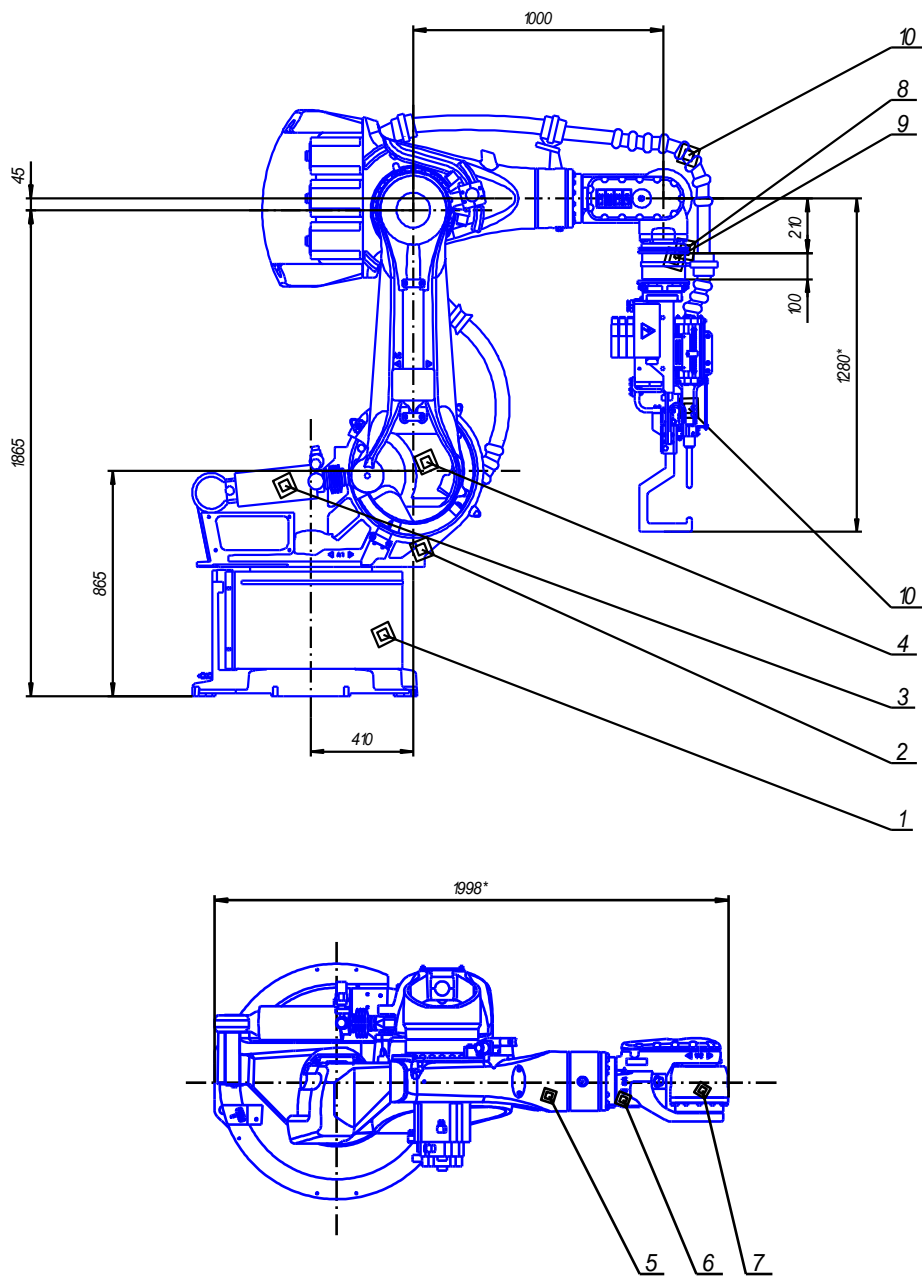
Манипулятор комплектации №1 с С-образными сварочными сервоклещами
